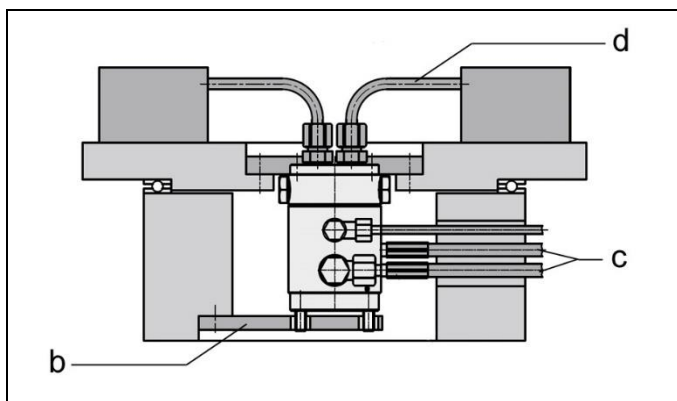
Possibilités d'installation et de connexion - connexion par tuyauterie
